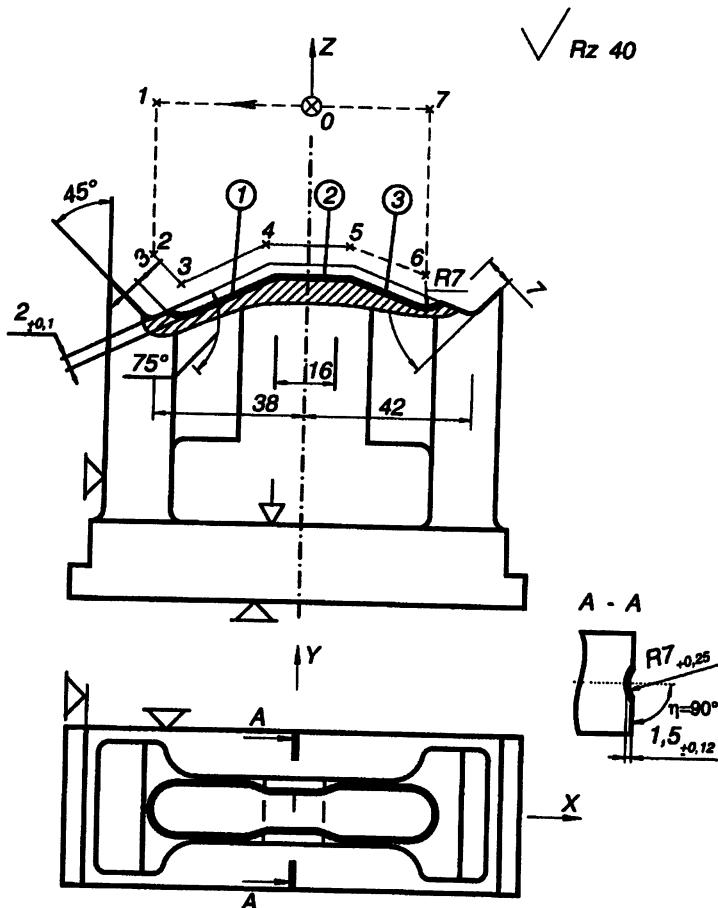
Эскиз детали для примера нормирования операции объемного фрезерования
